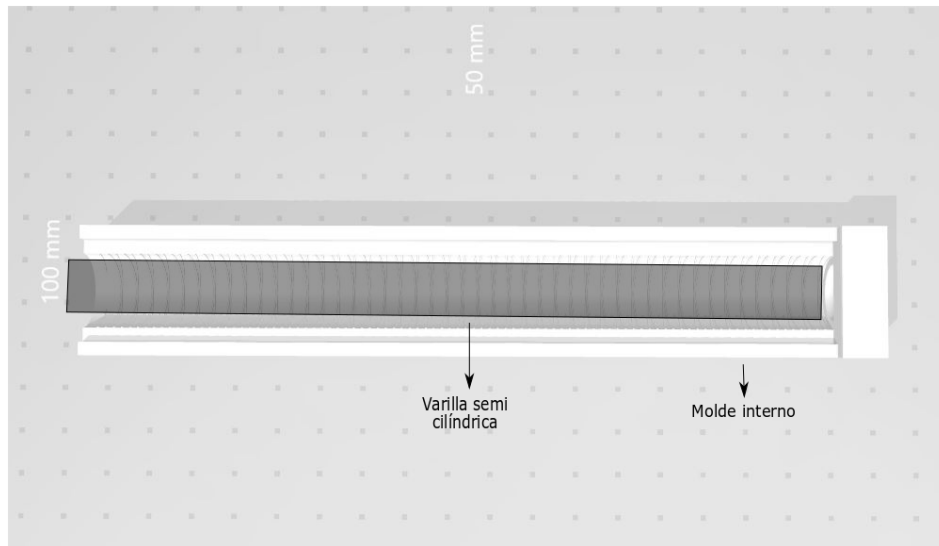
Paso 1 manufactura actuador del fibra reforzada: molde capa interna, diseñado para elaborar la cavidad interna del actuador con troquelado impreso sobre la cara interna para guía de costura.
